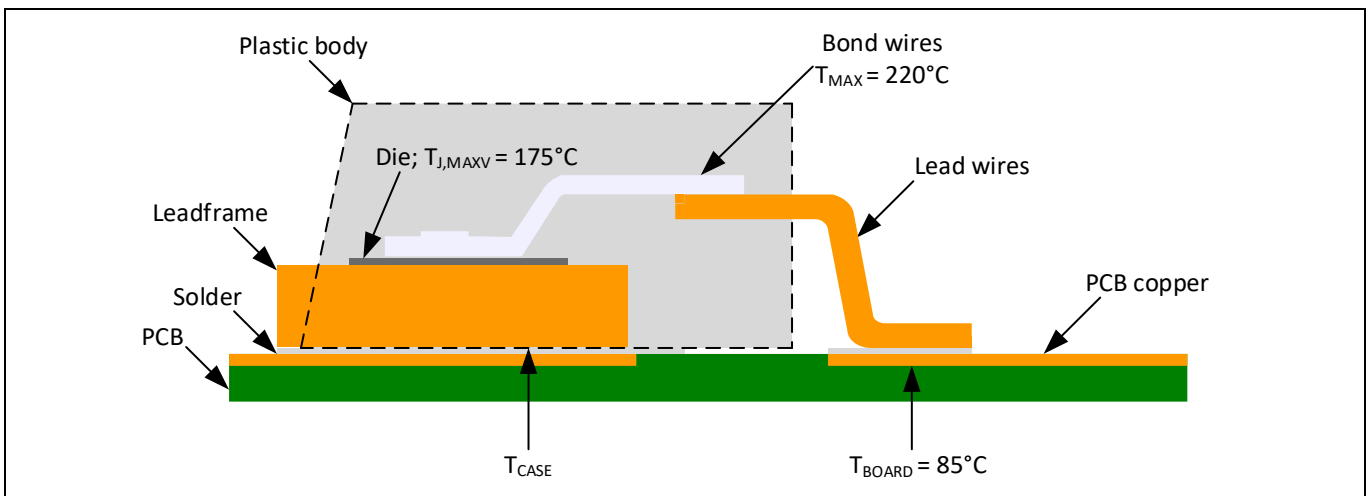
在 PCB 上安装的 D²PAK SMD MOSFET 封装剖面图
